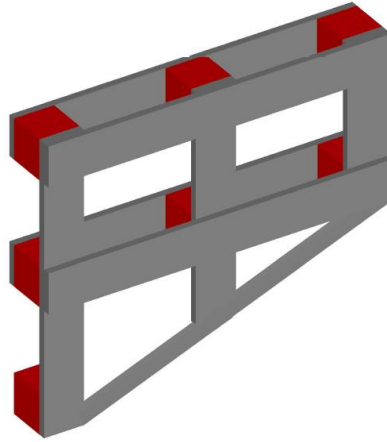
Pallet en diagonal proyecto I-BEAM
